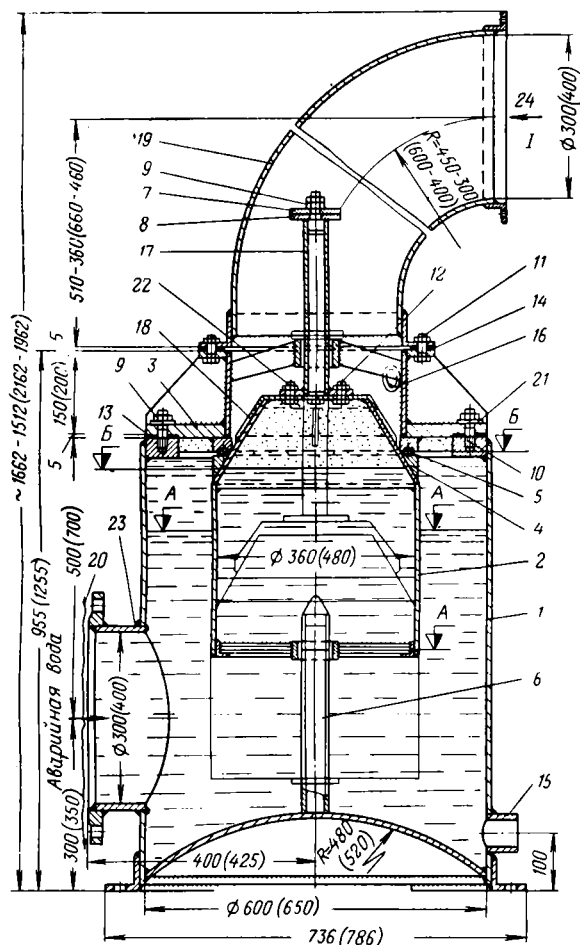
IX. Аварийный поплавковый клапан ЦА-3 и ЦА-4 для воздуховодов (в скобках даны размеры для ЦА-4):
